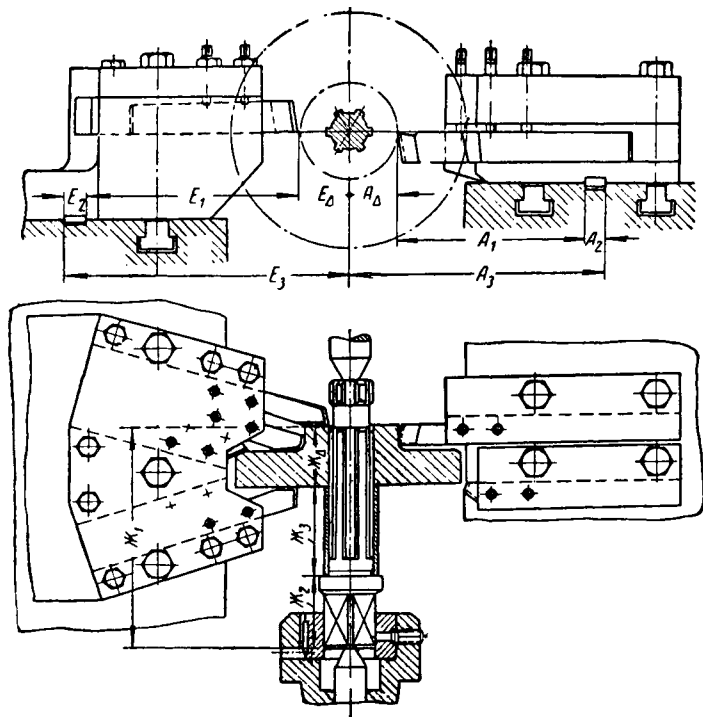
Схема настройки токарного многорезцового полуавтомата, не имеющего устройств для регулирования положения резцов
